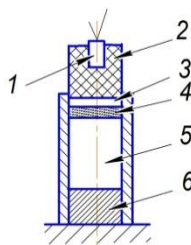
Схема установки обработки материалов высокоскоростным потоком частиц, метаемых торцевой поверхностью заряда ВВ через воздушный зазор, 1 – детонатор, 2 – заряд ВВ, 3 – воздушный зазор, 4 – навеска порошковых частиц, 5 – ограничивающий канал, 6 – заготовка
